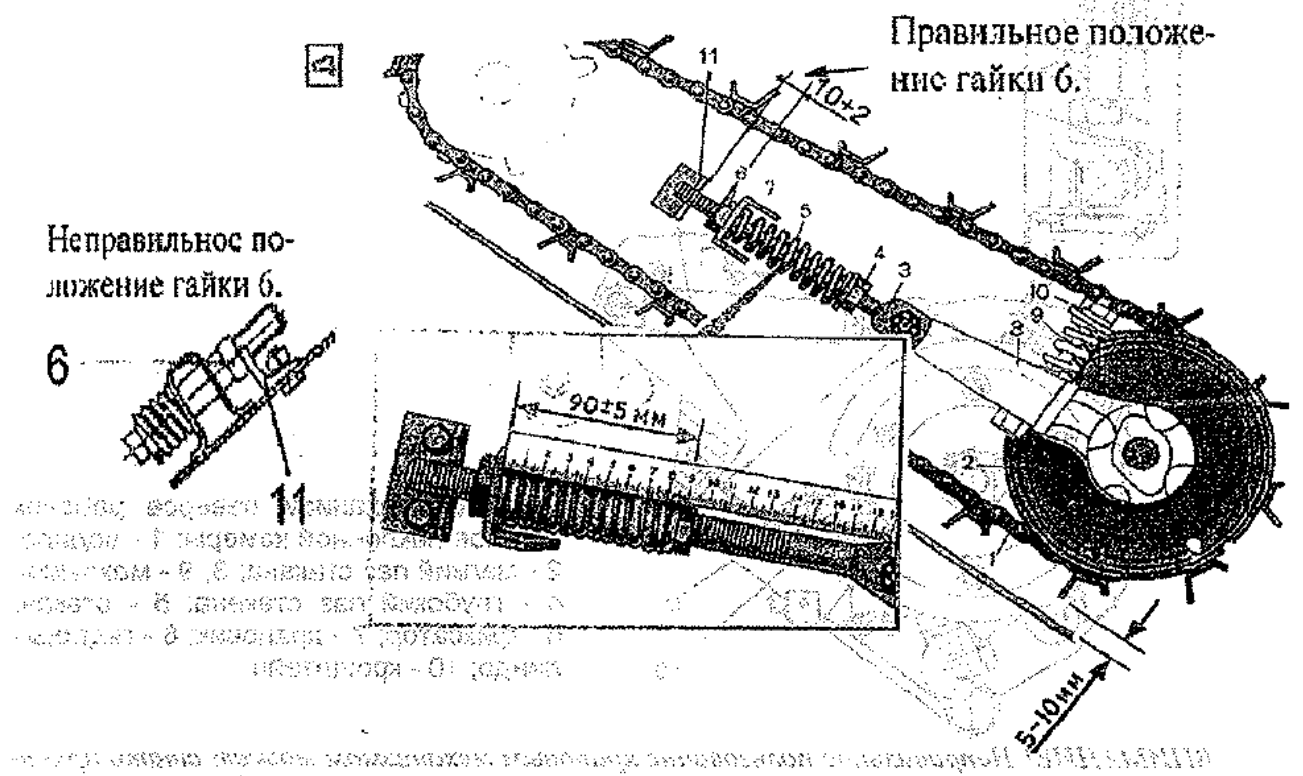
Схема регулировки транспортера: 1 – цепь; 2 – барабан нижний; 3 – винт натяжной; 4, 6 – гайка; 5 – пружина; 7 – кронштейн; 8 – опора; 9 – подвеска; 10 – шайба
